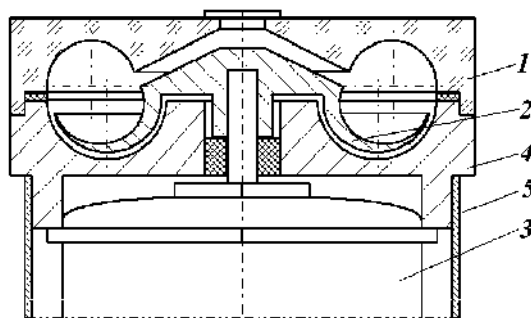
Центробежно-вихревая машина: 1 – статор-крышка; 2 – ротор; 3 – электродвигатель; 4 – корпус; 5 – кожух.
